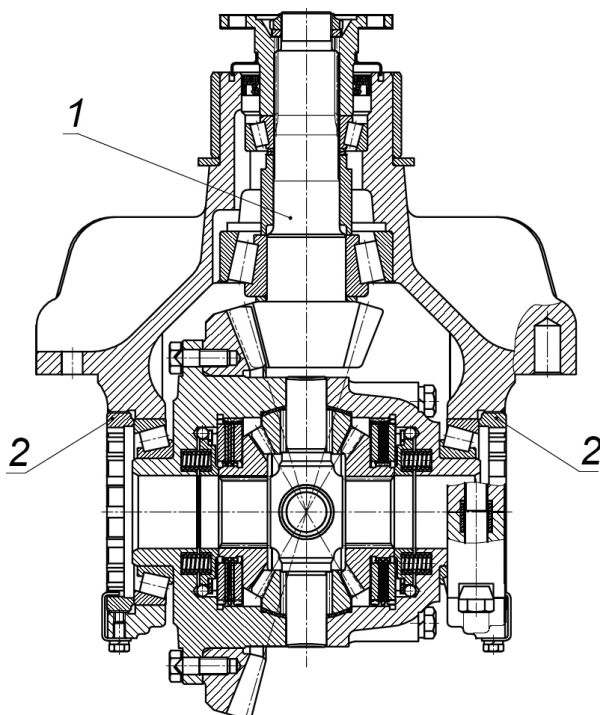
Ведущая шестерня в корпусе центрального редуктора
